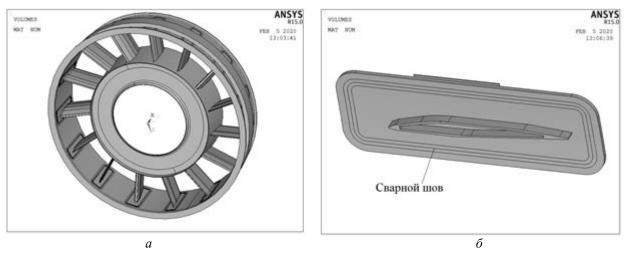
Общий вид геометрии узла авиационного двигателя (a) и фрагмент геометрии со сварным швом (б)
